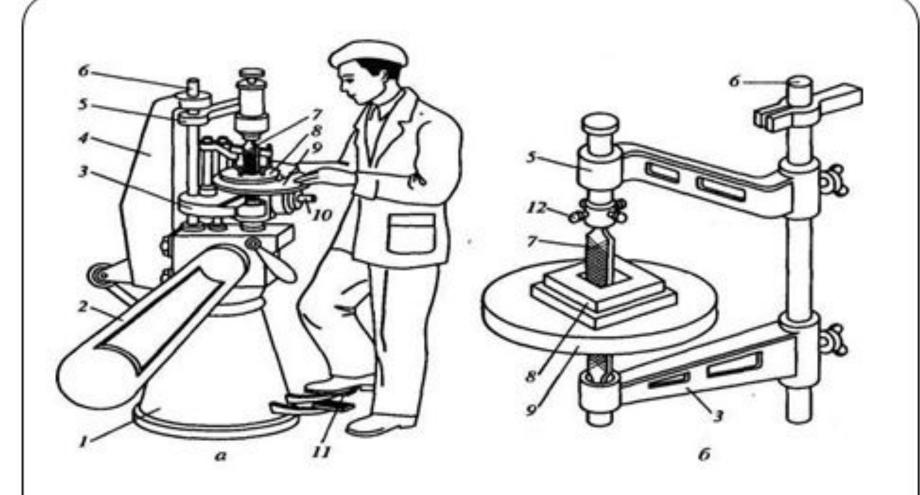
Стационарный опиловочно-зачистной станок: а - общий вид станка; б - исполнительный узел; 1 - станина; 2 кожух; 3,5- кронштейны; 4 - стойка; 6 - шток; 7 - напильник; 8 -
